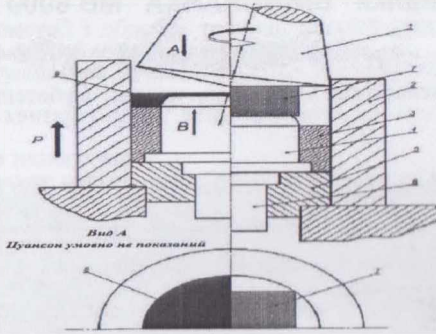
Схема налагоджування для штампування обкочуванням плоских циліндричних заготовок: 1 - нуансон; 2 - контейнер; 3,4- матриця; 5 - кільце; 6 - виштовхувач; 7 - вихідна заготовка; 8 - готова деталь.
